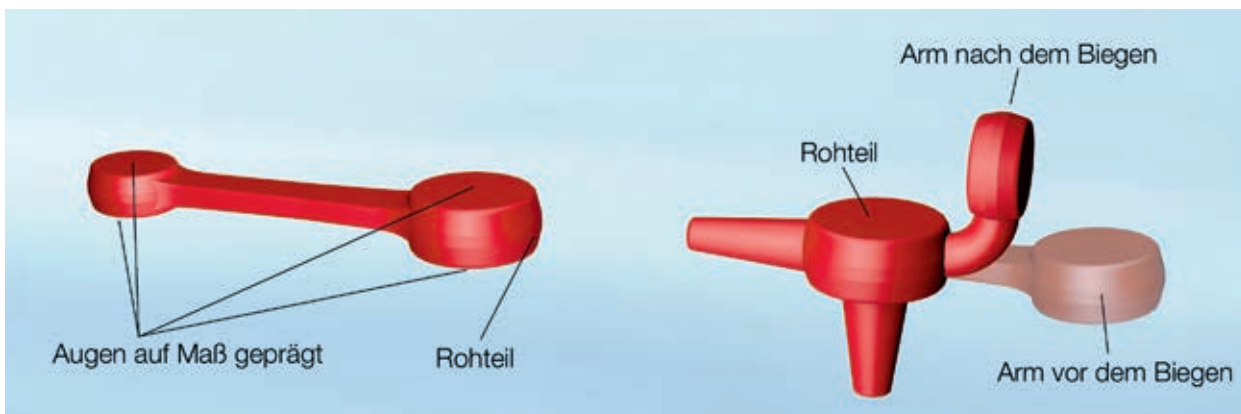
Partielles Nachformen durch Maßprägen (links) und Biegen (rechts)
